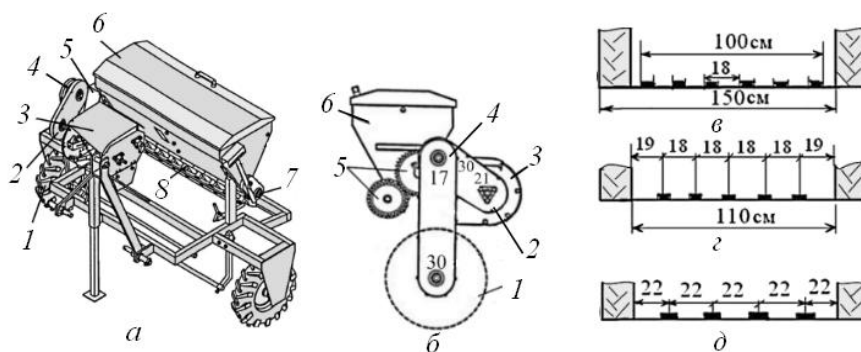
Сеялка для питомников «Эгедаль» тип 83: а – общий вид сеялки; б - схема привода; в, г, д – схема посева ленты, соответственно, шести, пяти и четырех строчная; 1 – приводное колесо; 2 – цепная передача; 3 – редуктор; 4 – цепная передача; 5 – зубчатая передача; 6 – бункер для семян; 7 – вал высевающего аппарата с цепным приводом ворошилки; 8 – высевающий аппарат
